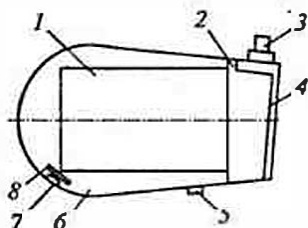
Конструкция массажного прибора «Харьковчанка»
